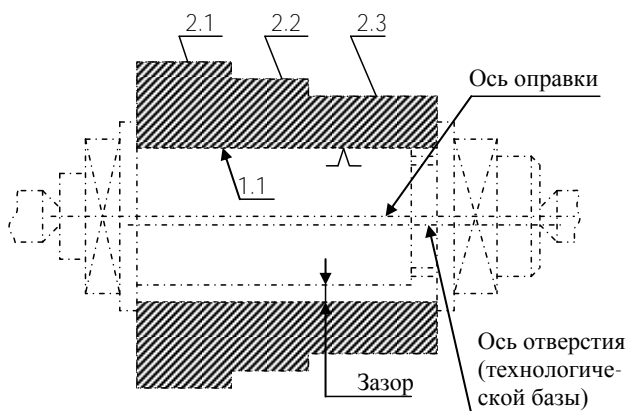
Схема базирования ступенчатой втулки на гладкой цилиндрической оправке с зазором
